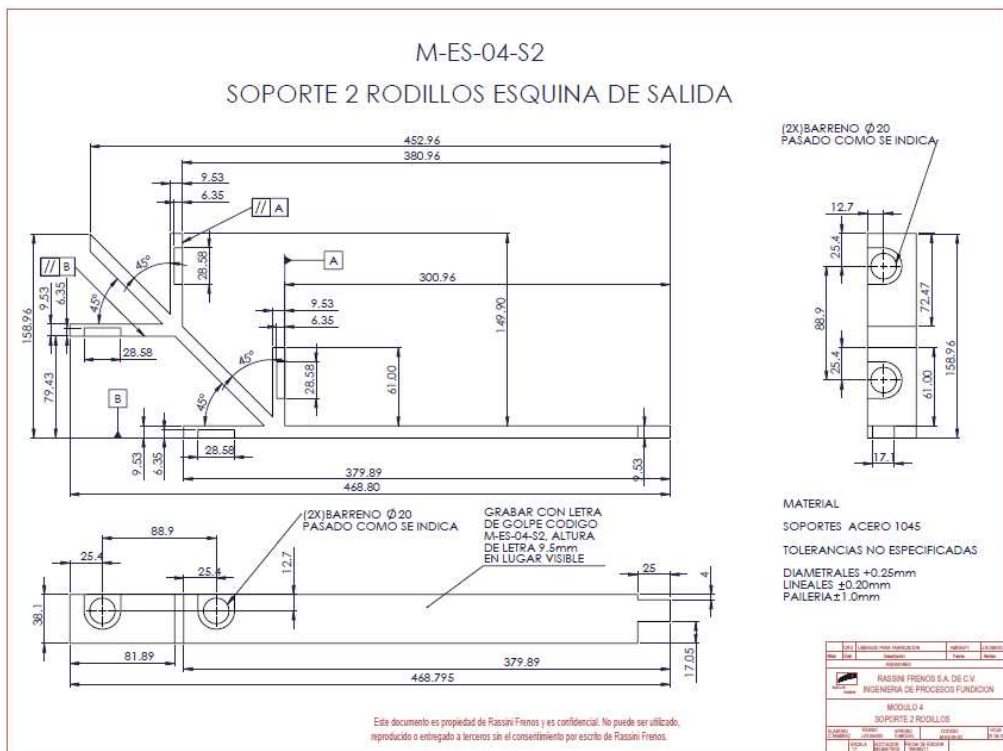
Plano de fabricación soporte 2 para rodillos
